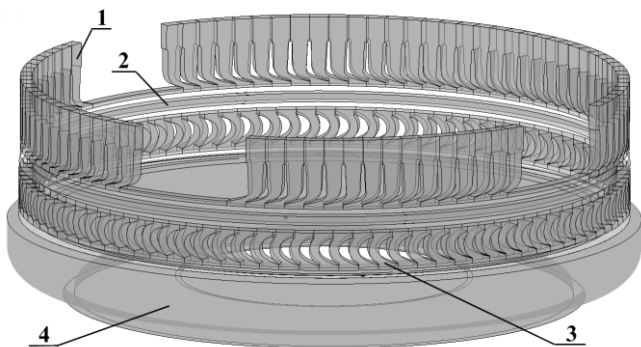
Розрахунковий об'єм: 1 – соплова решітка; 2 – міжвінцевий зазор; 3 – робоча решітка; 4 – вирівнююча камера
